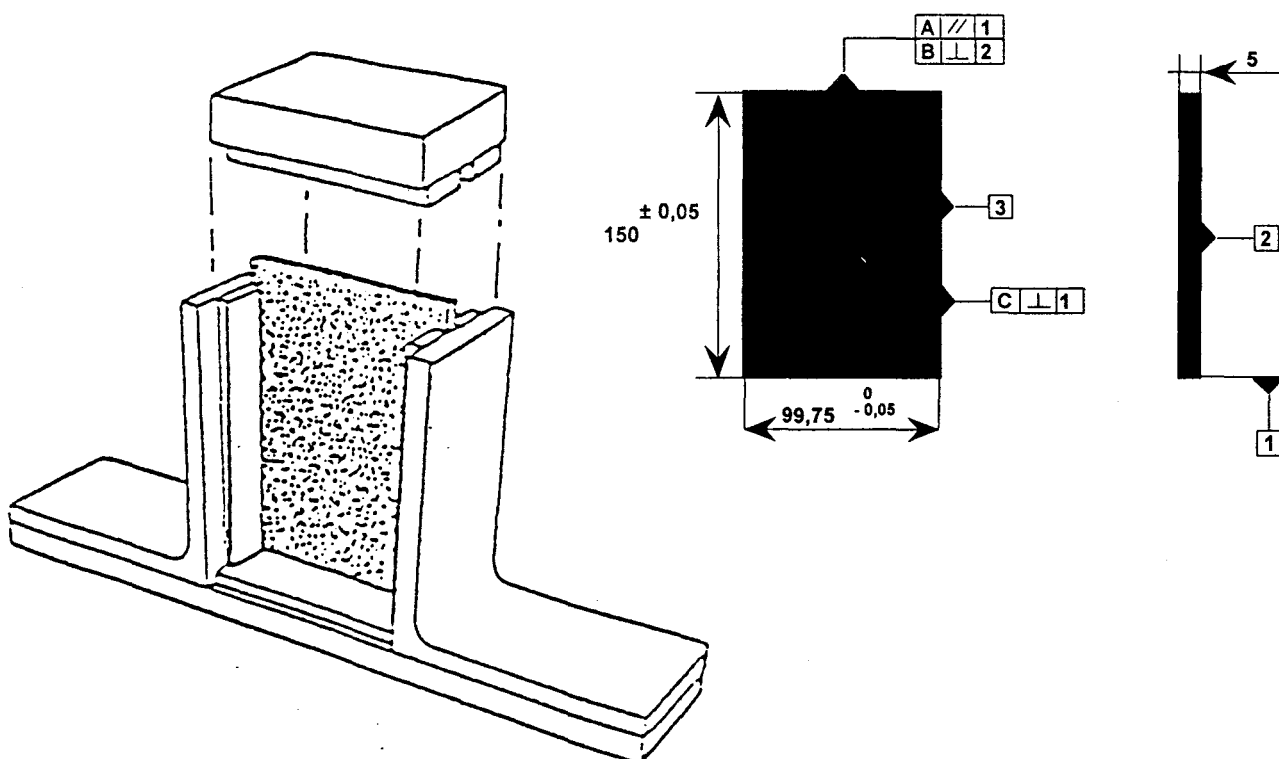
Essai de compression BOEING et géométrie des éprouvettes
